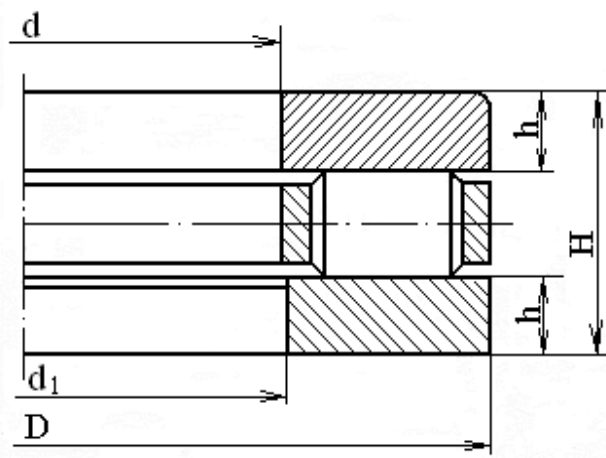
Подшипник роликовый упорный, однорядный
